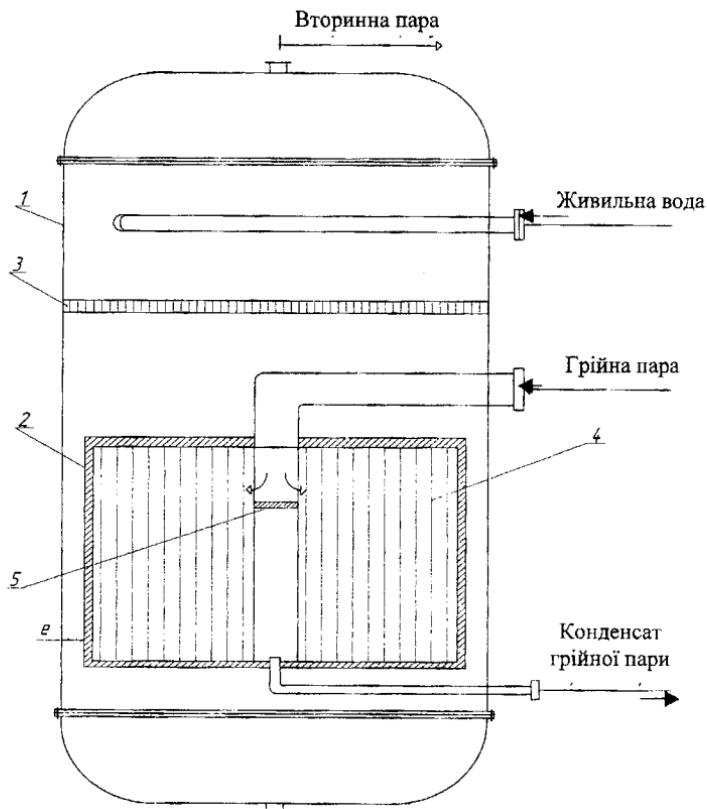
Принципова схема випарника: 1 – корпус; 2 – корпус грійної секції; 3 – дірчастий лист; 4 – випарні труби; 5 – напрямна перегородка
